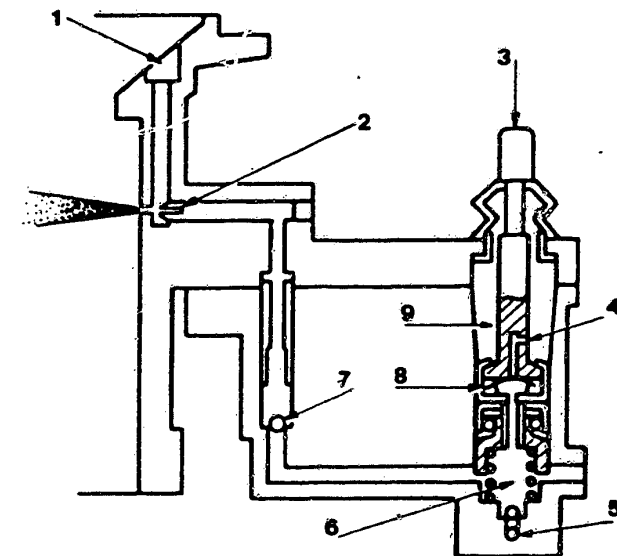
Die Beschleunigerpumpe und ihre Besonderheiten: 1 Beschleunigerpumpen-Düsenentlüftung - 2 Beschleunigerpumpendüse - 3 Pumpenkölbchen - 4 Rücklaufbohrung - 5 Einlassventil - 6 Pumpendruckkammer - 7 Auslassventil - 8 Bimetall-Rücklaufventil - 9 obere Kammer.
